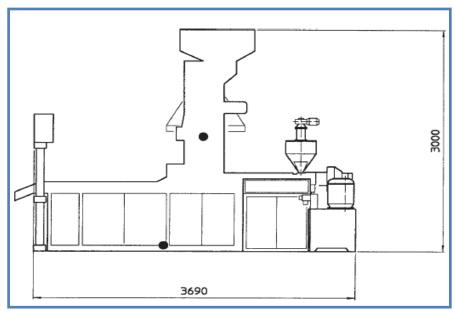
IMAGEN XXVIII: DIMENSIONES DE LA MÁQUINA
